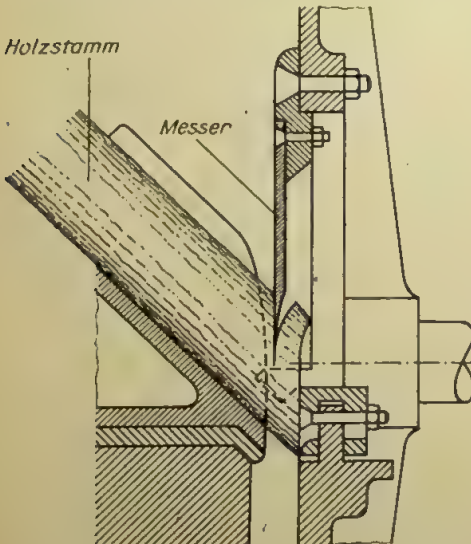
Wirkprinzip einer Hackmaschine
